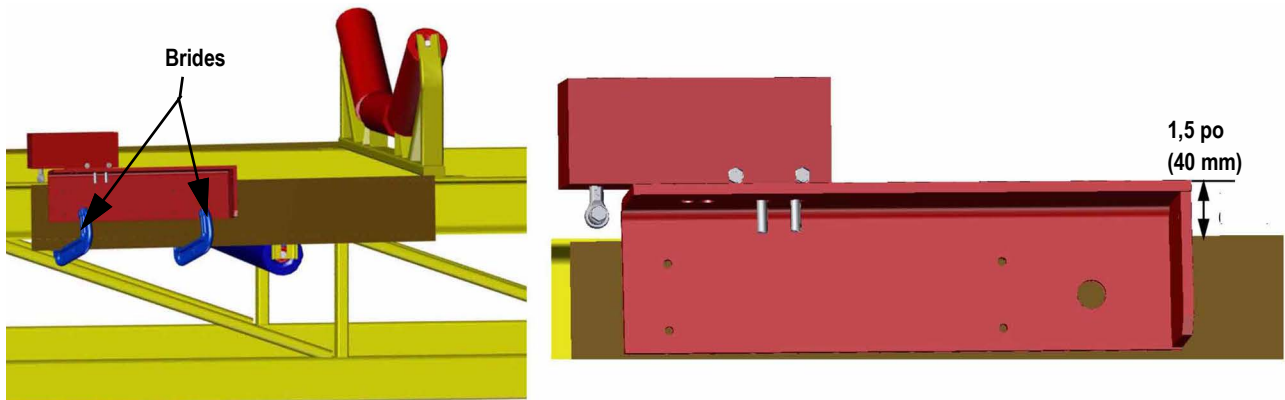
Utilisez des brides pour positionner l'ensemble soudé
